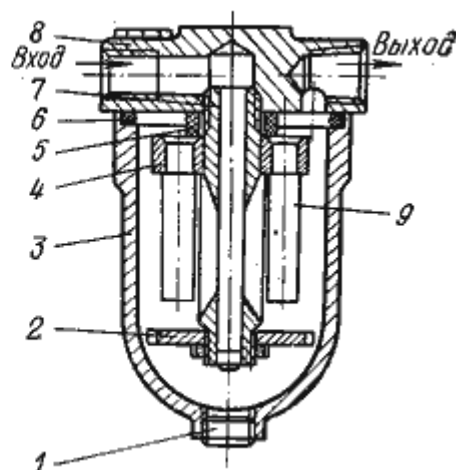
Магнитный фильтр типа С43-3: 1 - пробка; 2 - латунная шайба; 3 - корпус; 4 - шайба; 5 - прокладка; 6 - уплотнение; 7 - латунная труба; 8 - крышка; 9 - магниты
